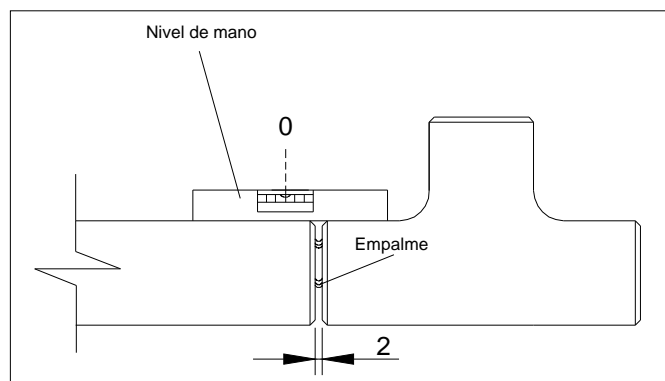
Apuntalado o fijación cañería v/s Te de conexión.
